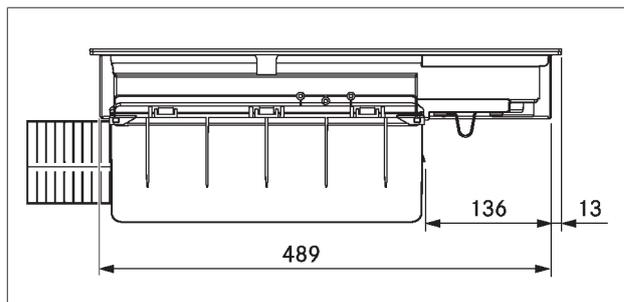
Dimensions CKA2/CKA2AB - Vue latérale
